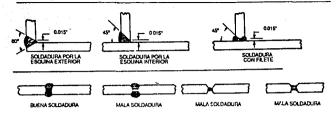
Uniones para la soldadura por gas. (Ref. 2)
